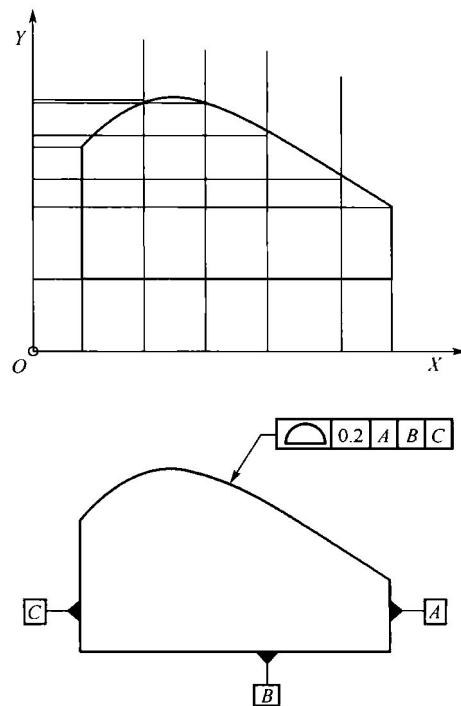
尺寸公差和几何公差对于异型特征的定义
